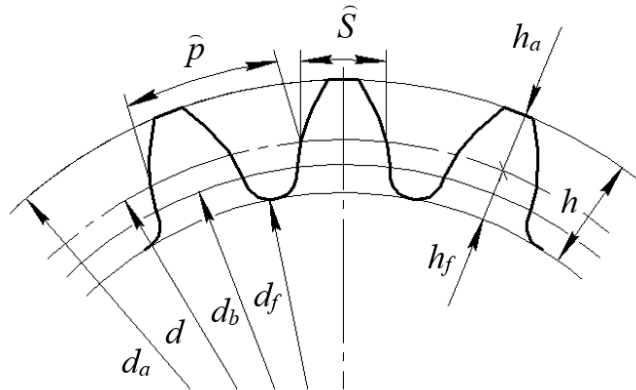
Геометрические параметры эвольвентного зубчатого колеса
